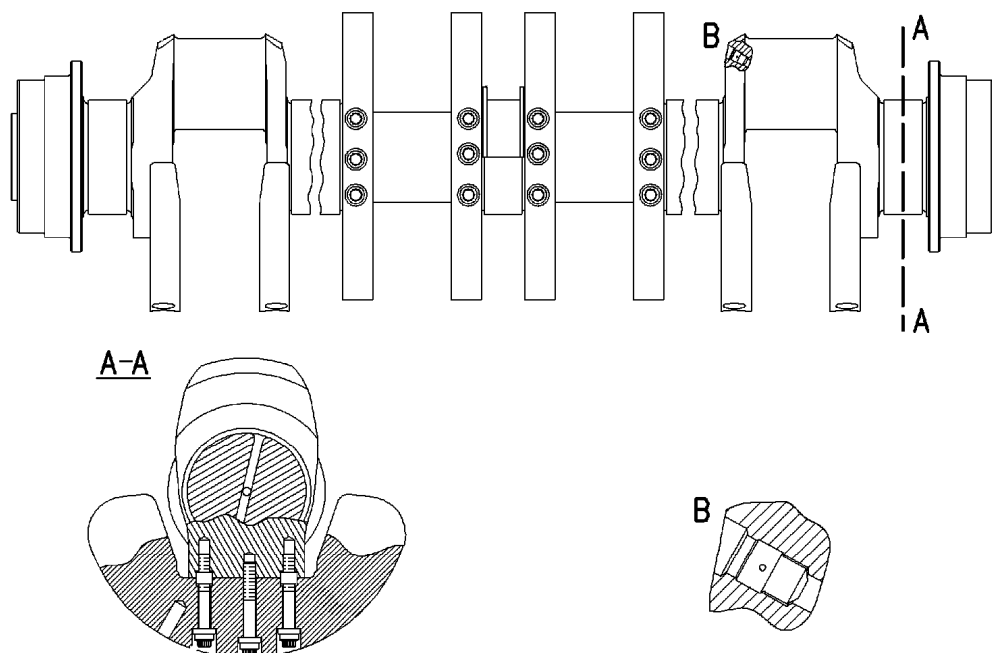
Колінчатий вал двигуна Cat 3516 [3]
